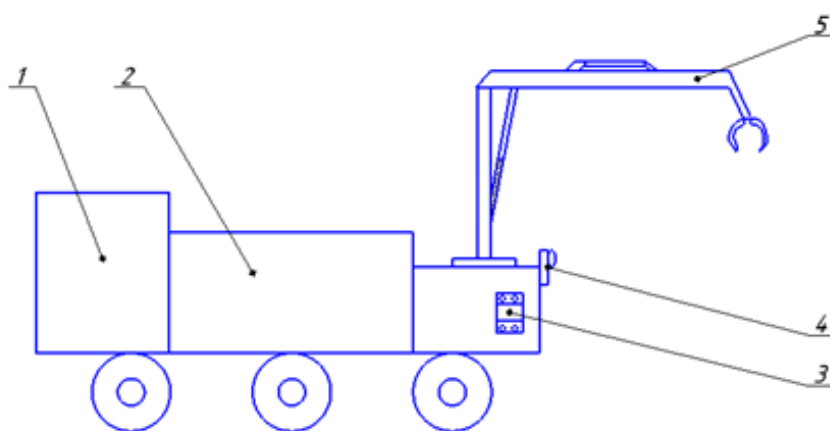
Основные части конструкции робота: 1 – блок управления и емкость для аккумуляторов; 2 – кузов для сбора образцов; 3 – камера для наблюдения положения руки 4 – газоанализатор; 5 – рука для сбора образцов
